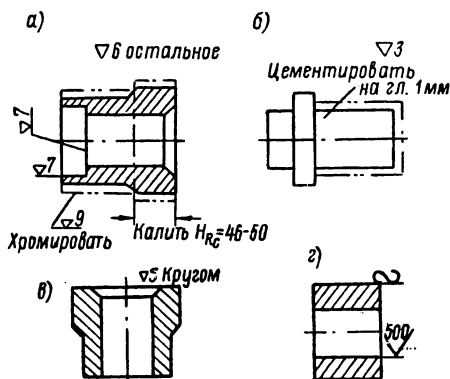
Примеры обозначения шероховатости поверхности на чертежах.
